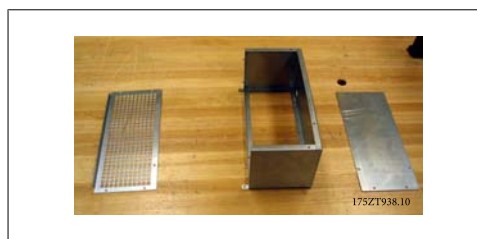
Частично собранный верхний воздуховод с кронштейном преобразователя частоты
